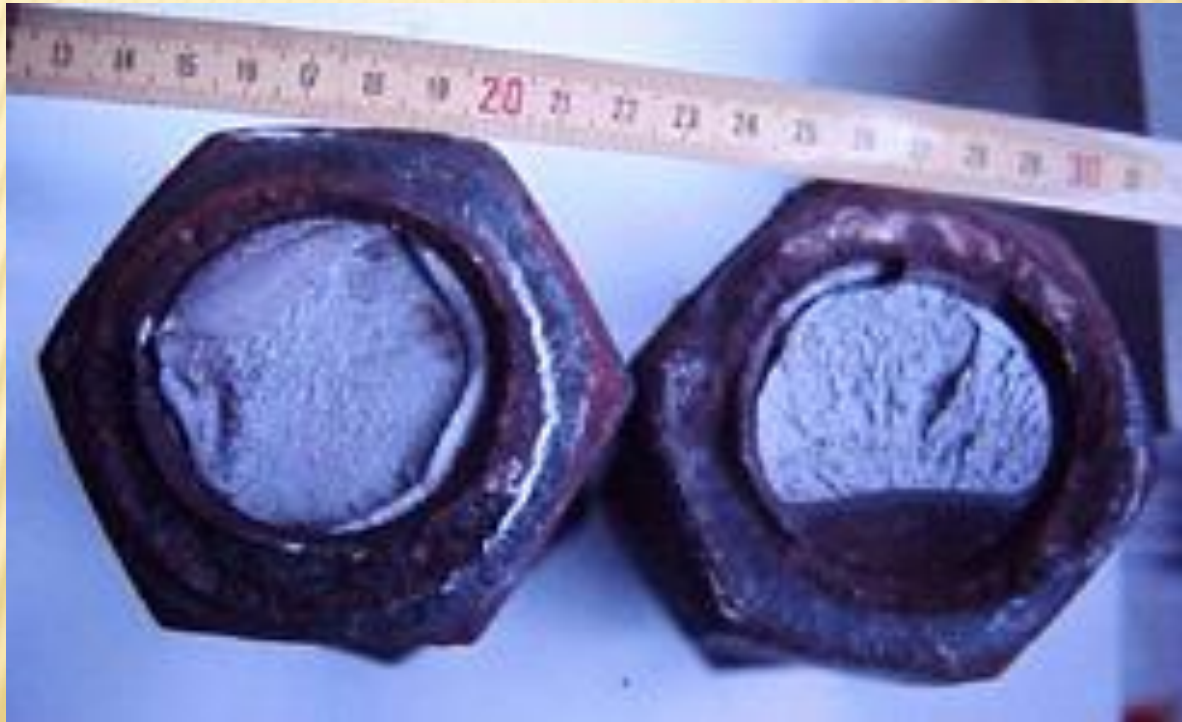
Corrosion fissurante sur assemblage boulonné de tige d'ancrage
